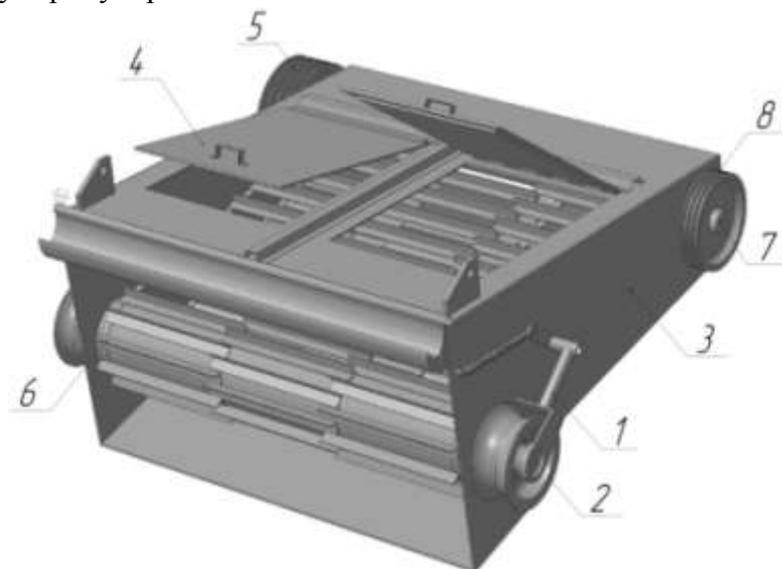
Модель наклонной камеры зерноуборочного комбайна: 1 – шкив натяжной; 2 – ведомый вал; 3 – корпус; 4 – крышка; 5 – шкив; 6 – транспортер цепной; 7 – верхний вал; 8 – шкив
